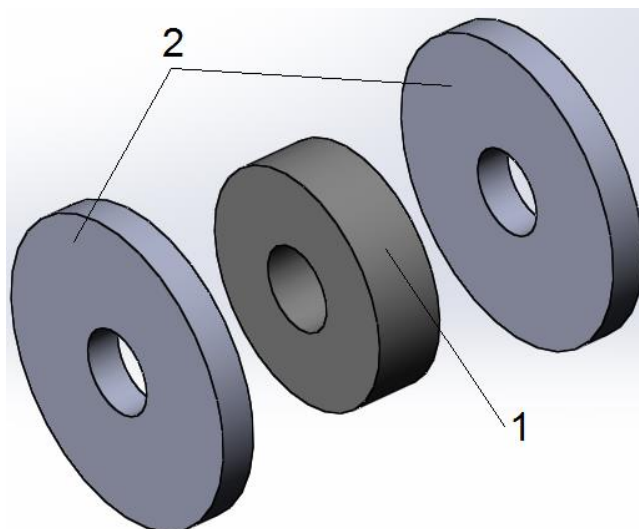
Составные элементы конструкции магнитного колеса: 1 – постоянный кольцевой магнит; 2 – опорные диски-магнитопроводы
